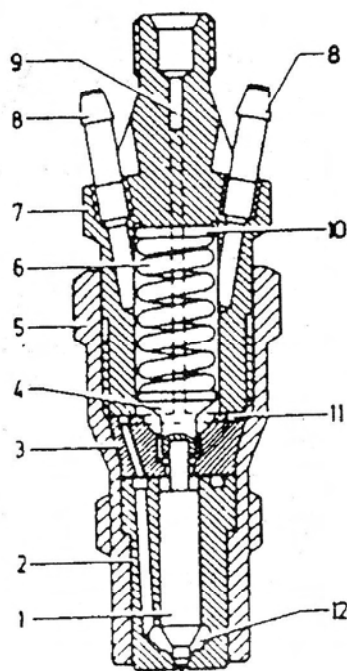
Разрез корпуса форсунки и форсунки (четырёхцилиндровый двигатель)
